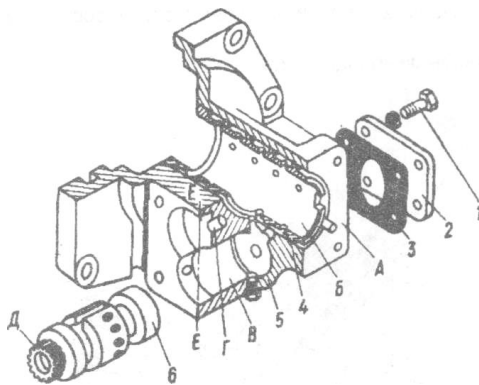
Складання гідророзподільника: 1 — болт; 2 — кришка; 3 — прокладка; 4 — втулка; 5 — корпус; б — золотник; А — торець; Б, В, Г — отвір; Д — мітка; Е-Е — вісь
